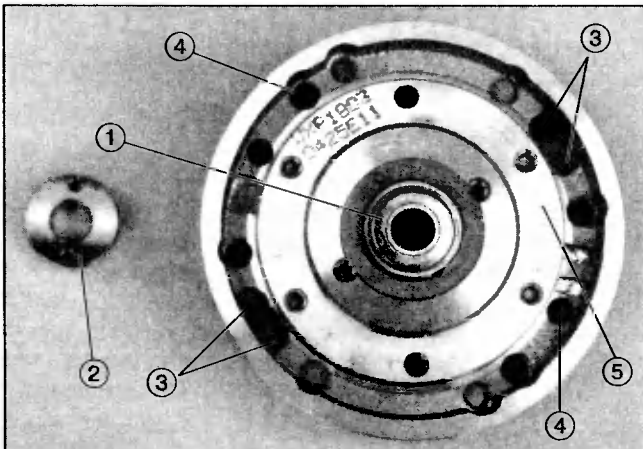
Верхний цилиндр VXP1803 (вид сверху)
